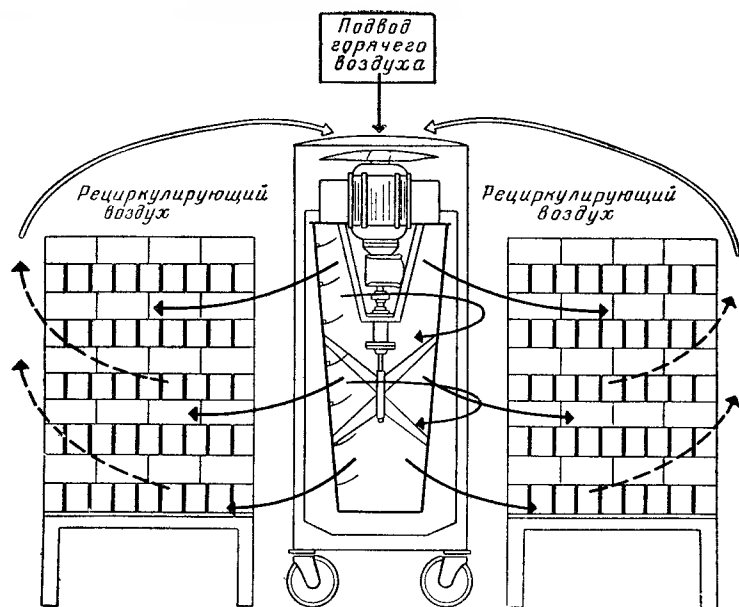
Сушилка с вращающимися струями, которая использует прямую рециркуляцию воздуха
